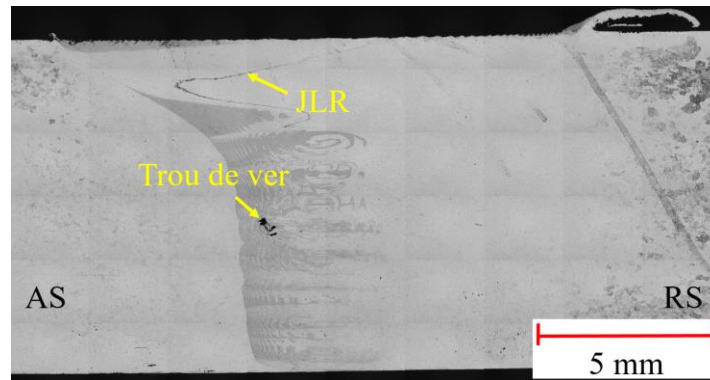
Macrographie d'une soudure en 6061-T6 de 9,5 mm
